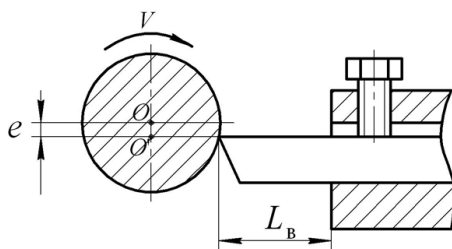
Схема подготовки поверхности под напыление методом нарезания «рваной» резьбы
